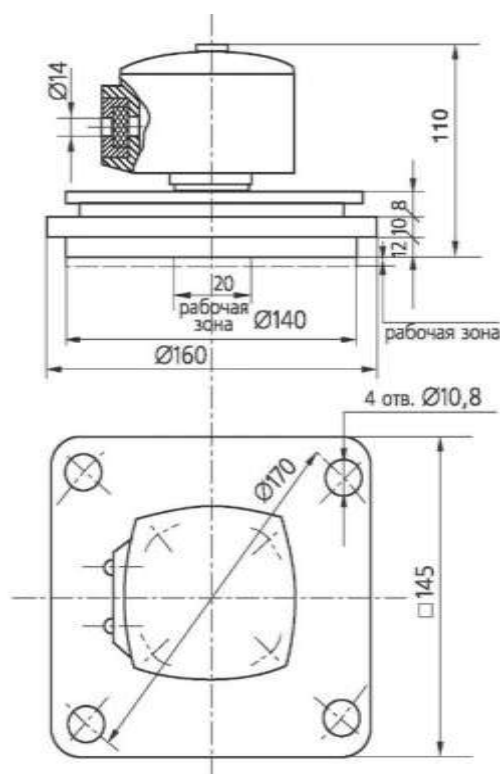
Общий вид, габаритные и установочные размеры СУС-181Р(Б)
